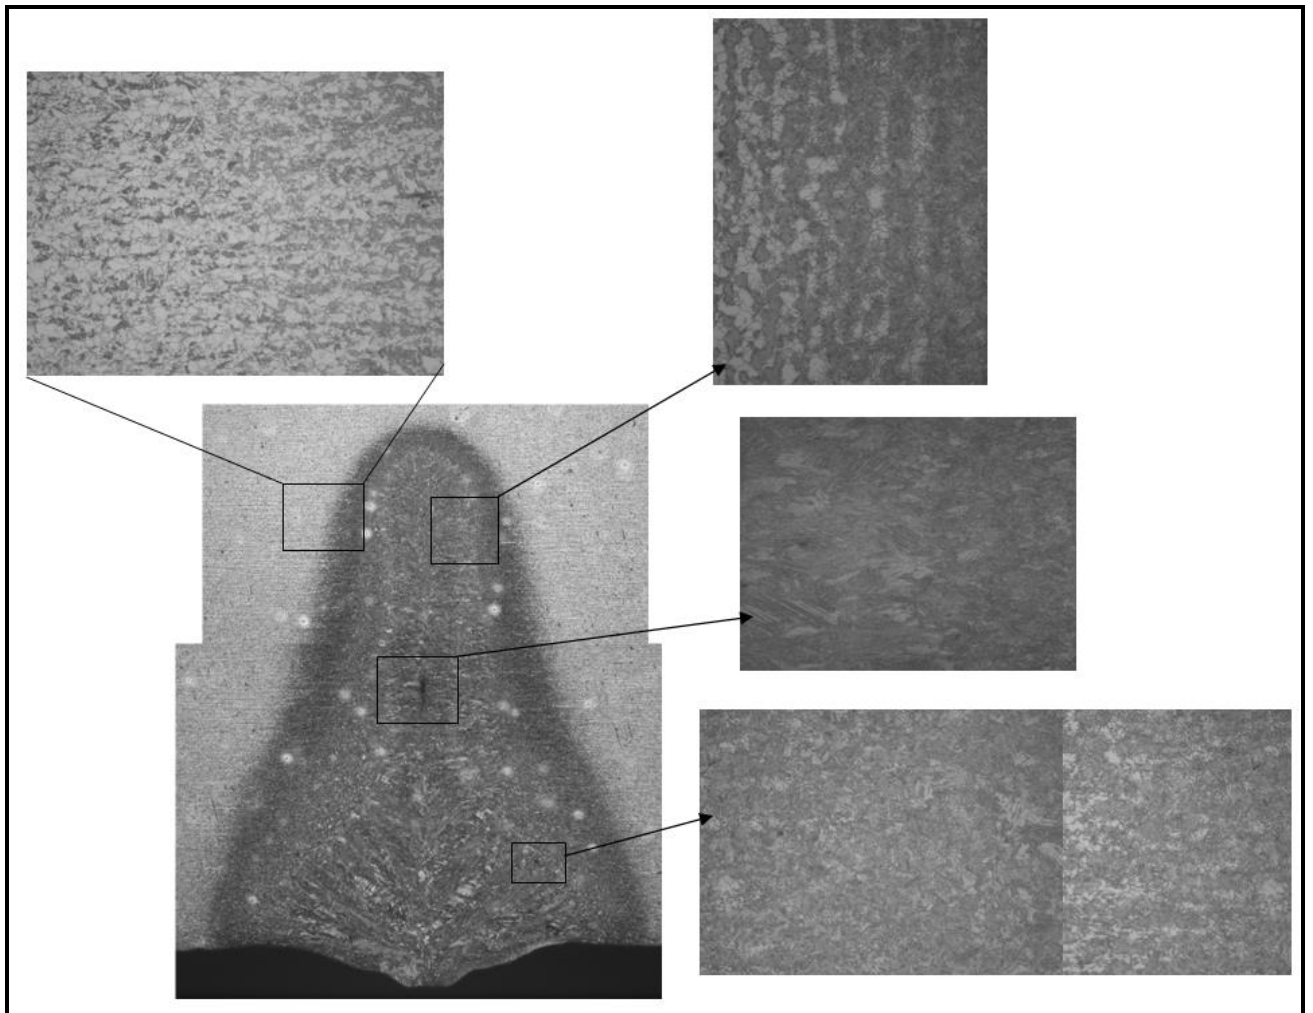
Загальний вид та будова структури зварного з'єднання: сталь 09Г2С
